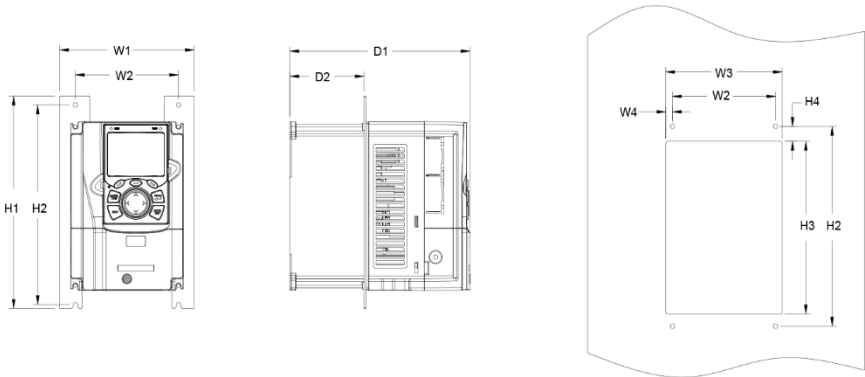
Схема фланцевого монтажу ПЧ напругою 380 В, потужністю від 1,5 до 75 кВт
